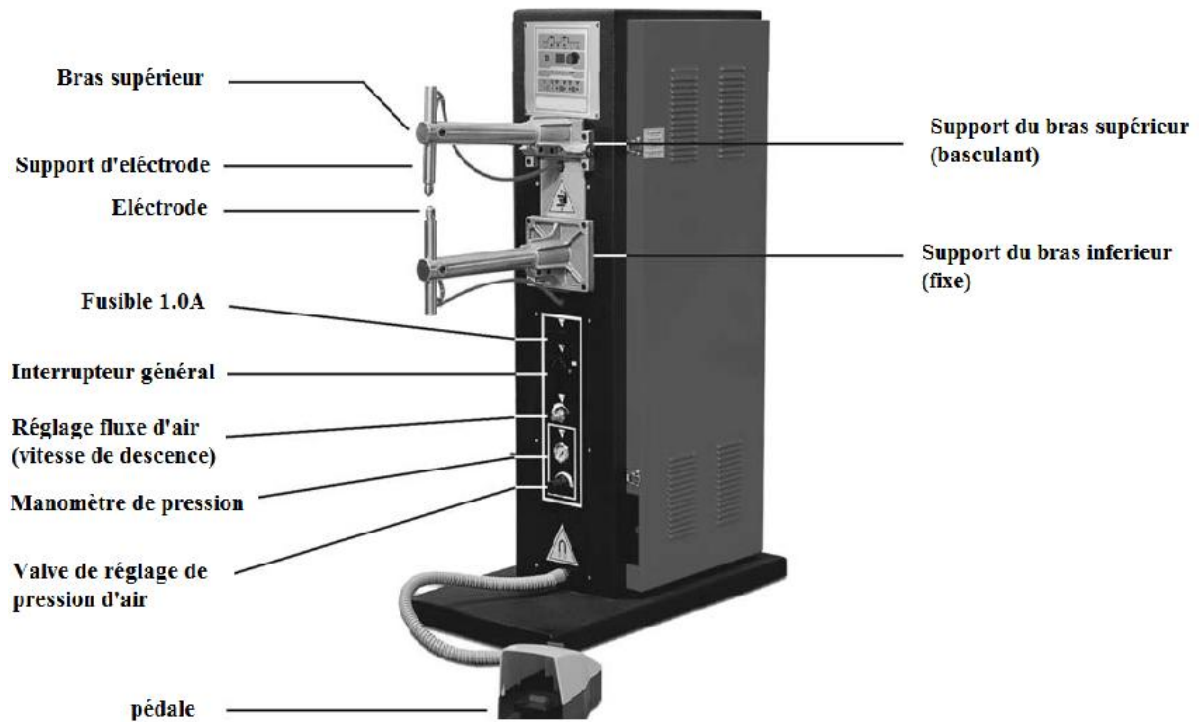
Description de la machine de soudage par point (THI 50 DIGIT)
